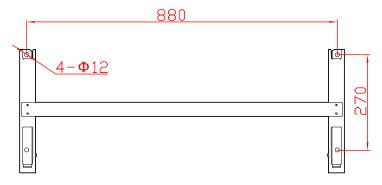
Dimensione dei fori di installazione (unità di misura: mm)
